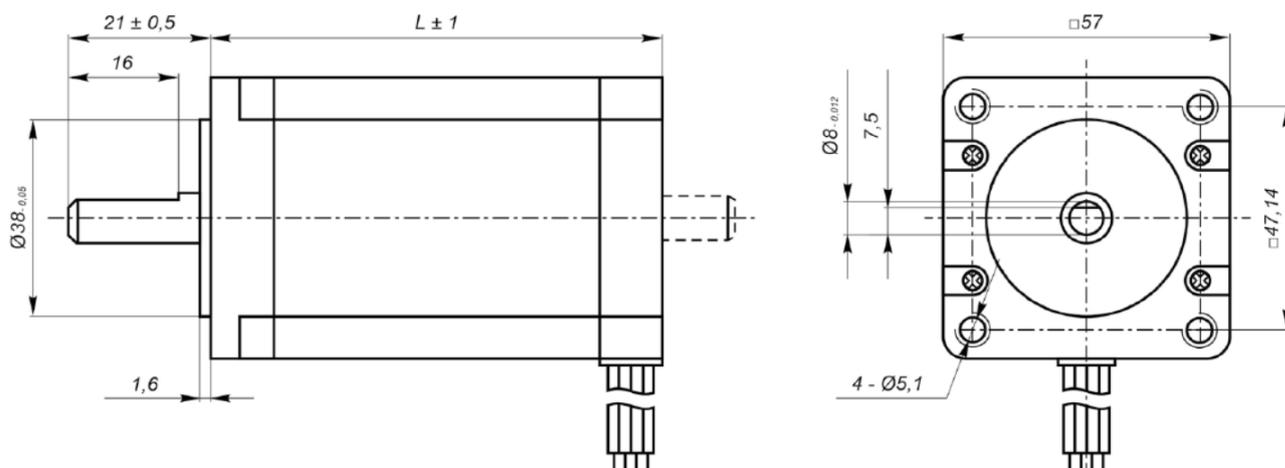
Габаритные и присоединительные размеры ST57-H76
